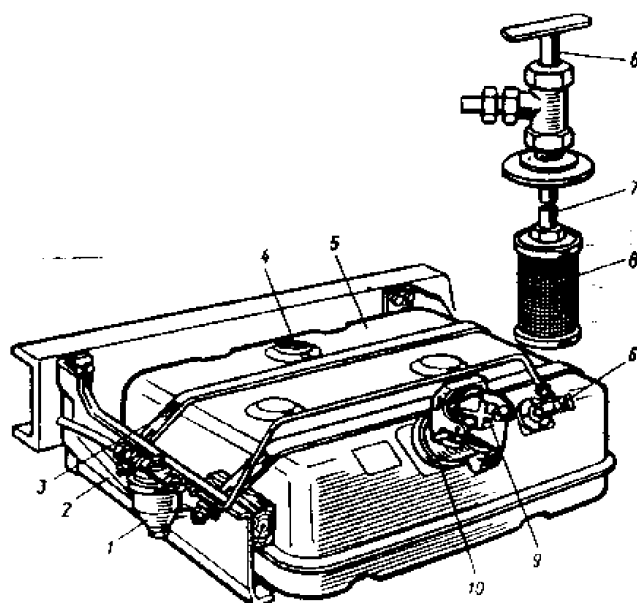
Топливный бак. 1-фильтр-отстойник; 2-кронштейн крепления бака; 3-хомут крепления бака; 4-датчик указателя уровня топлива в баке; 5-топливный бак; 6-кран; 7-приемная трубка; 8-сетчатый фильтр; 9-пробка бака; 10-горловина.
